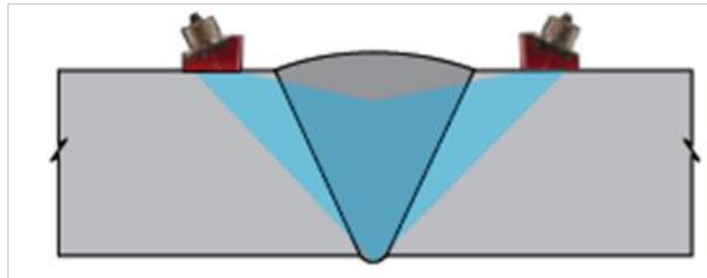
Inspección de una soldadura mediante la técnica TOFD.
